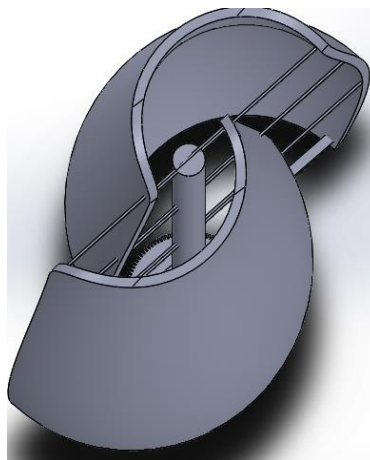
Dibujo vista superior de la turbina eólica de Tulipán. Diseñada en SolidWorks®.
